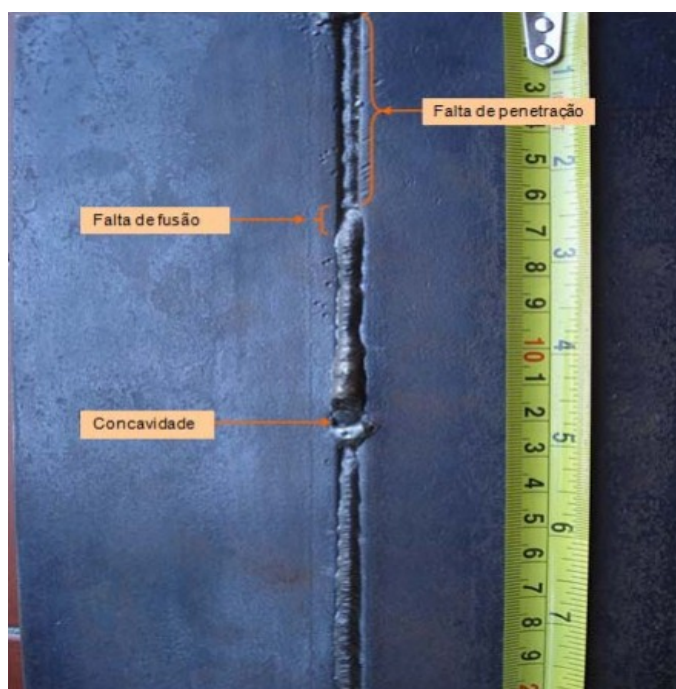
Descontinuidades em uma junta de topo soldada (raiz). Fonte: (FUNDAÇÃO BRASILEIRA DE TECNOLOGIA DA SOLDAGEM, [20--?])
